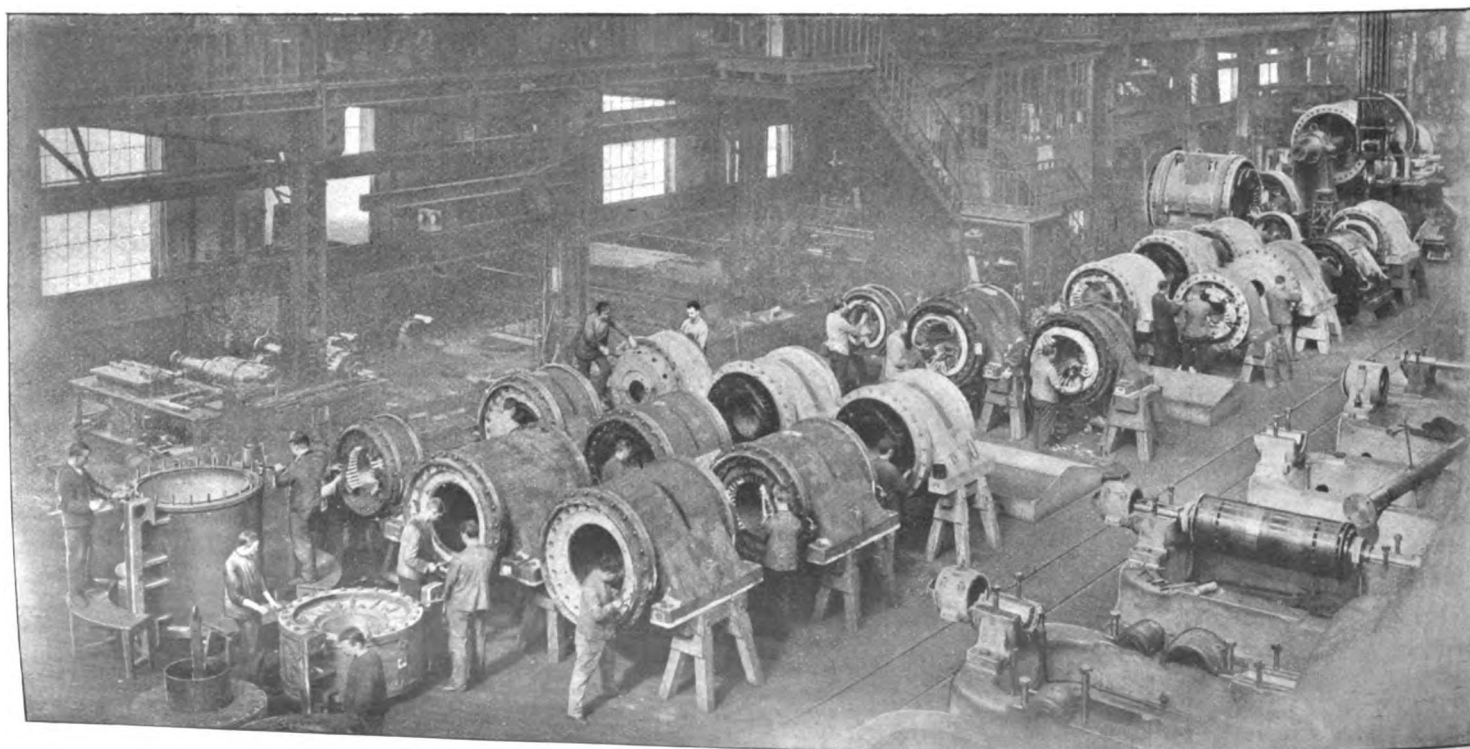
Werkstatt für Drehstrommaschinen-Gehäuse.
